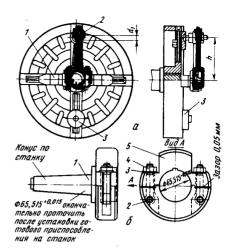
Приспособления для обработки баббитовой заливки подшипников:
